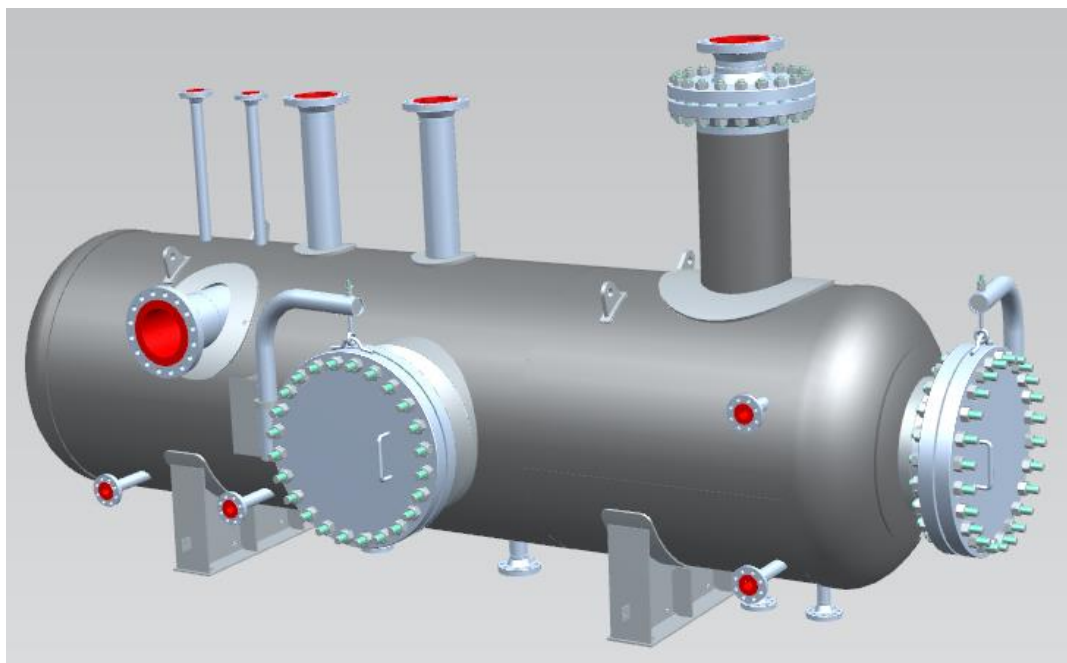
Equipo planteado para la primera prueba de exportación
